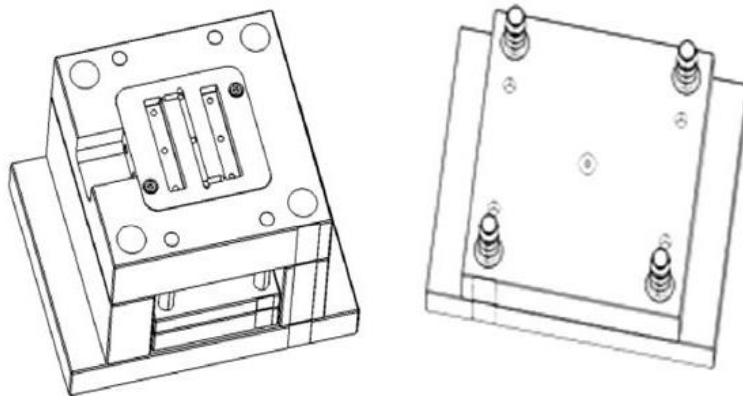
Desenho do molde para fabricação dos provetes (Imagem retirada de [2]).
